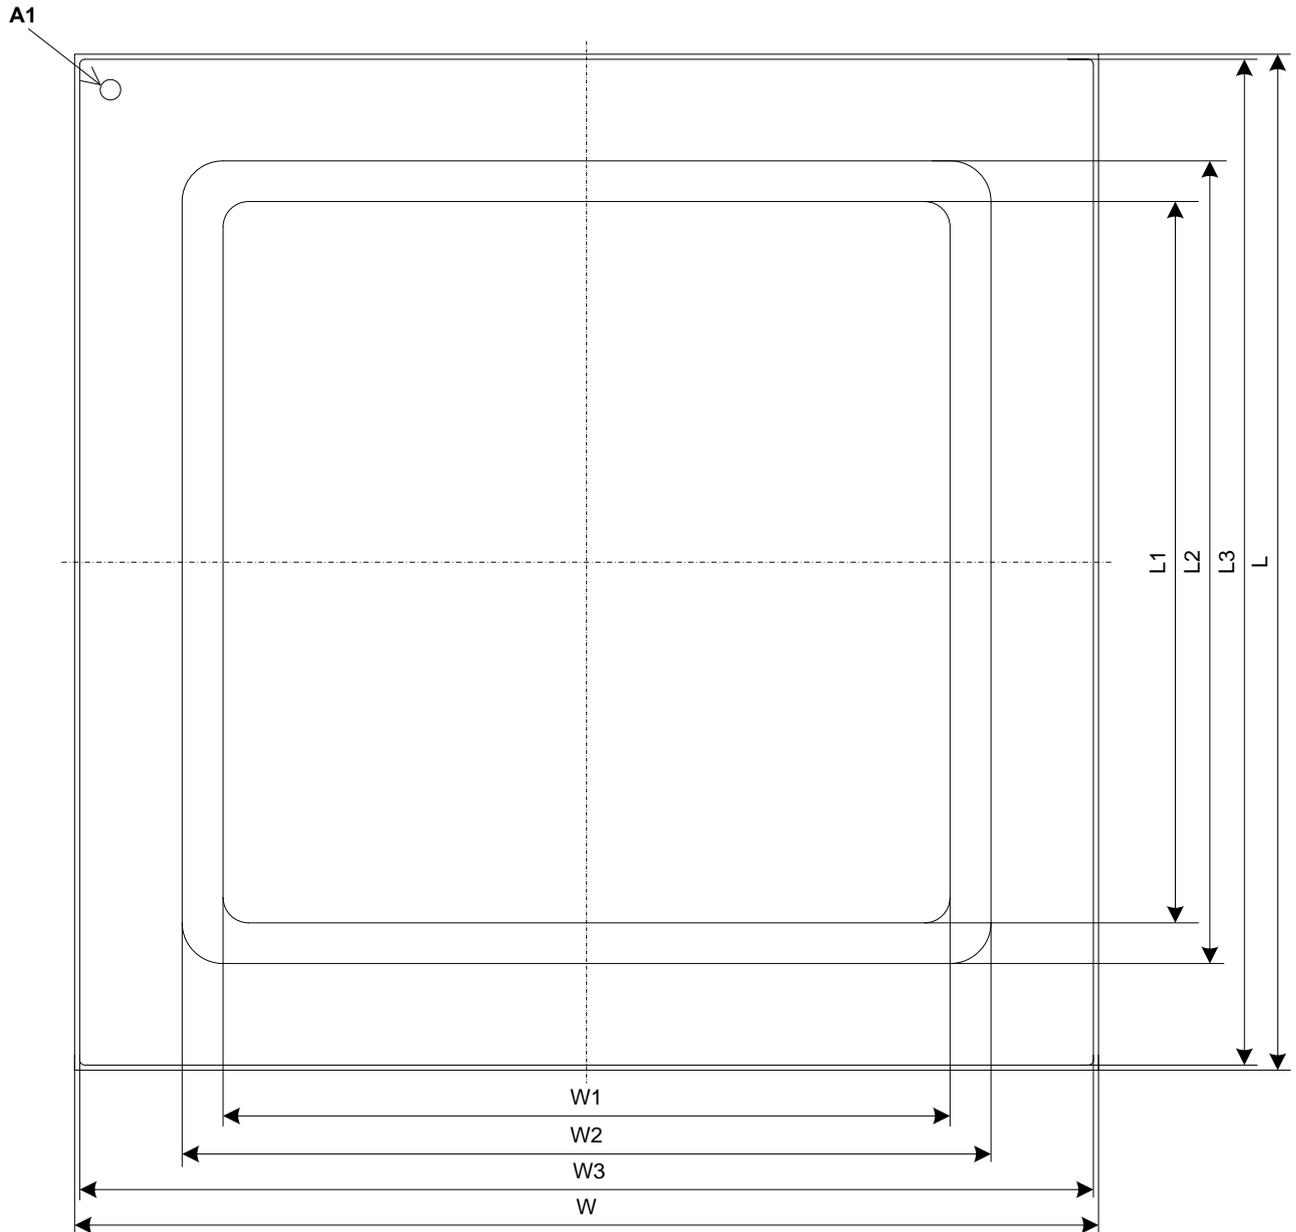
Корпус микропроцессора BE-M1000 (вид сверху)
